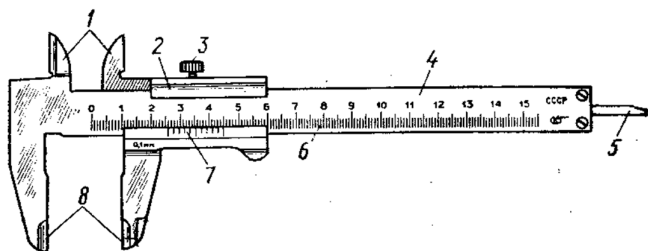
Штангенциркуль ШЦ-I: 1 – губка для внутренних измерений; 2 – рамка; 3 – зажим рамки; 4 – штанга; 5 – линейка глубиномера; 6 – шкала штанги; 7 – нониус; 8 – губка для наружных измерений
